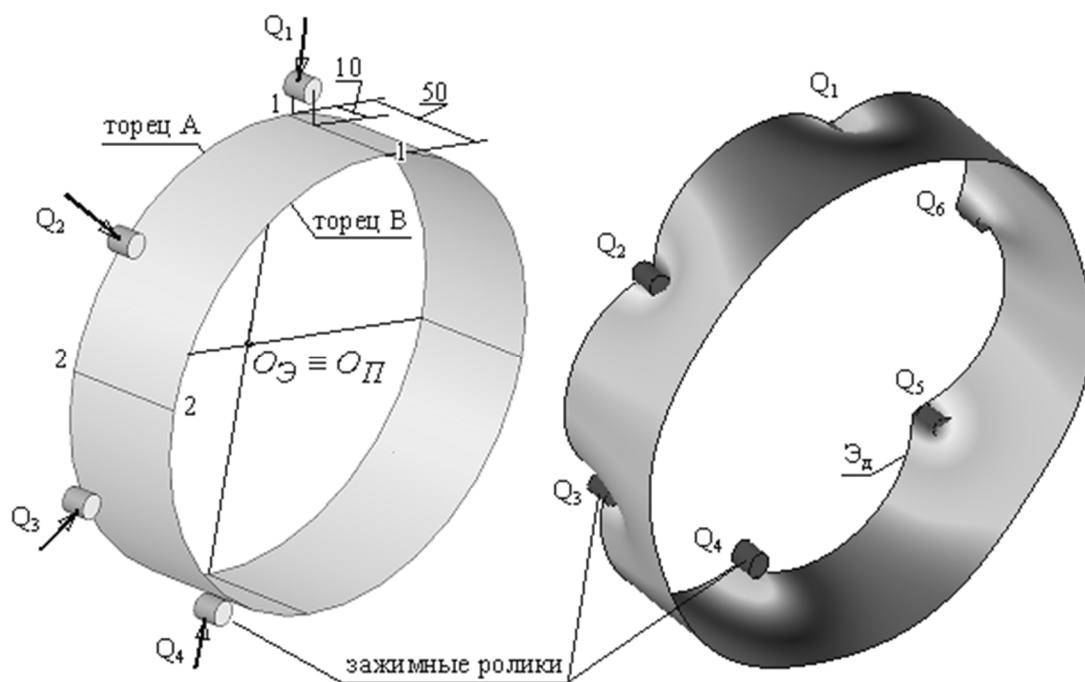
Модель закрепления заготовки в приспособлении с 6-ю зажимными роликами:
